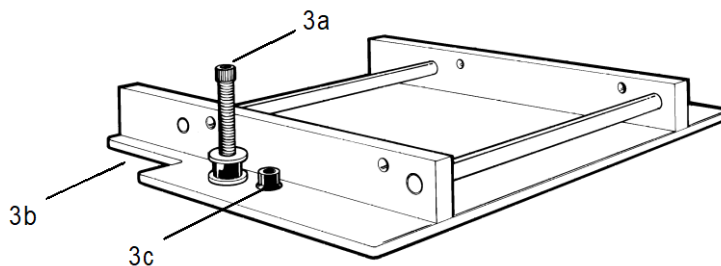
Optische Schienen mit Fixierschraube (3a), Einkerbung (3b) und Einstellschraube (3c)
